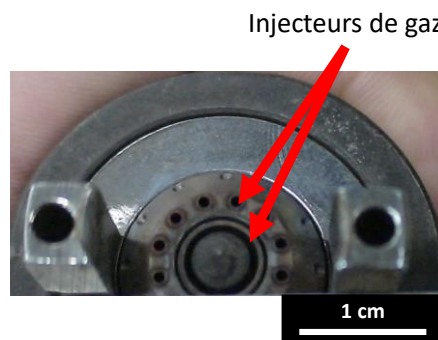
Photographie optique de la buse de la torche CastoDyn DS 8000 de Castolin Eutectic.
